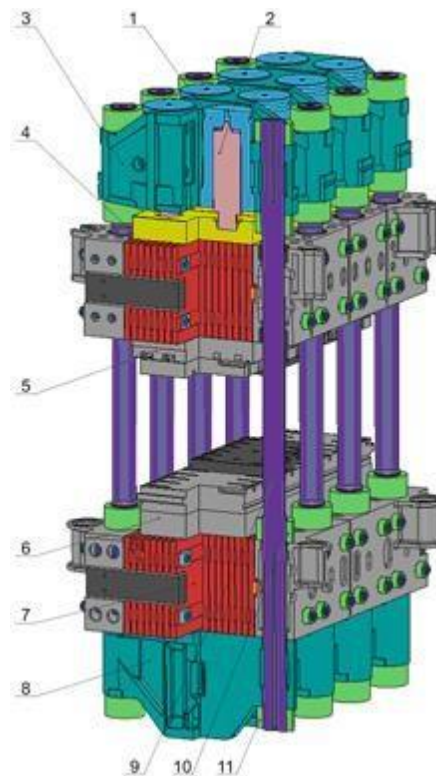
Гидравлический пресс конструкции УЗТМ силой 300 МН
